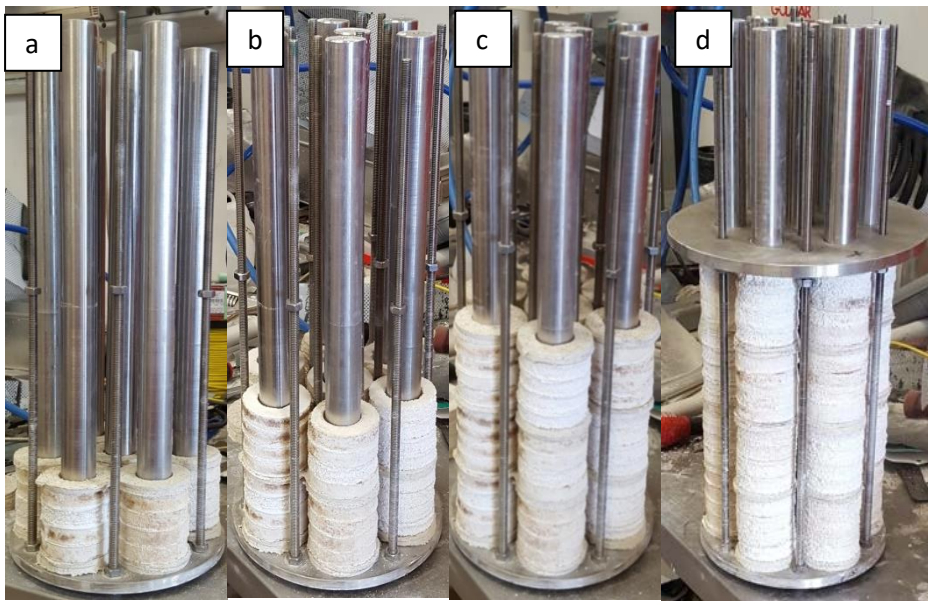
Varie fasi dell'assemblaggio del dispositivo filtrante
